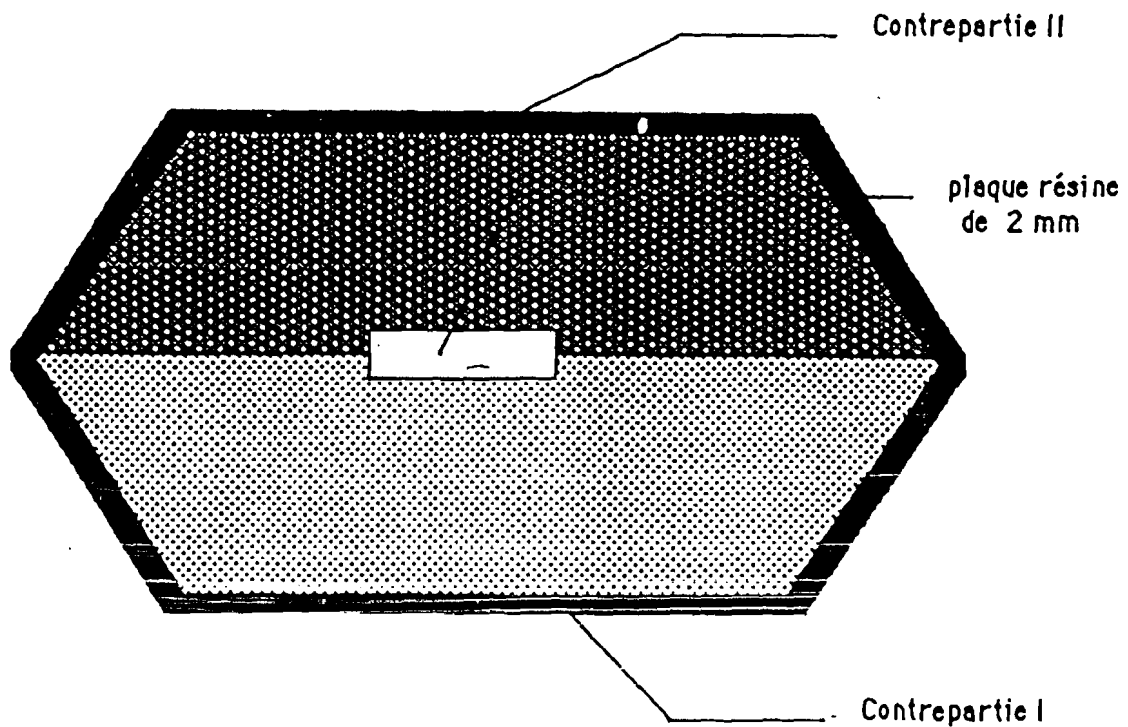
Plaque résine de 2mm, encore en moufle, obtenue après injection.
